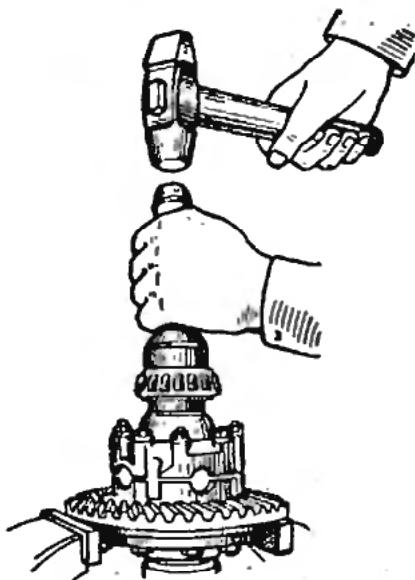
Напрессовка подшипников на шейки коробки сателлитов дифференциала
